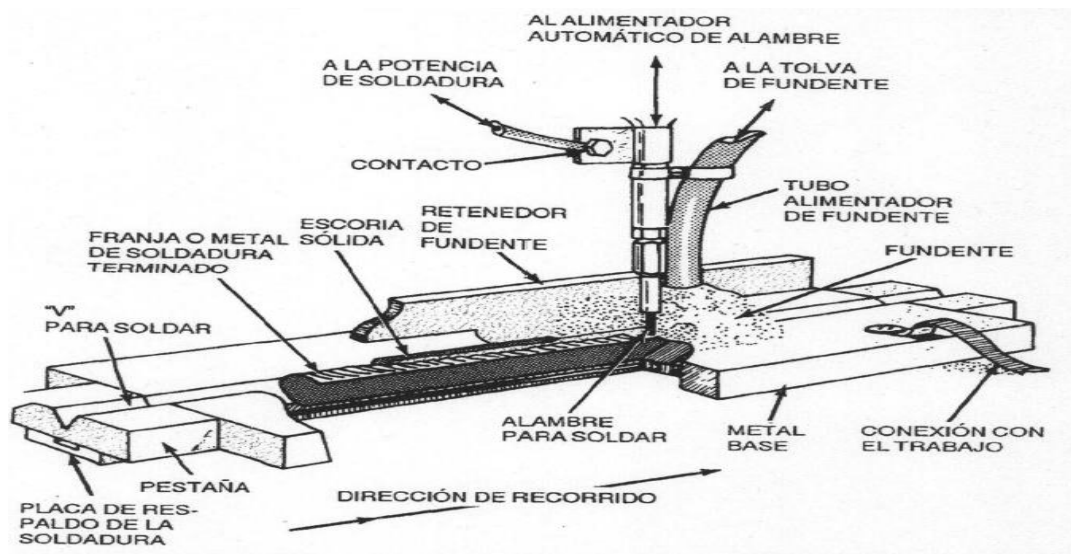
Equipo de un proceso de soldadura por arco sumergido (SAW) (15).
